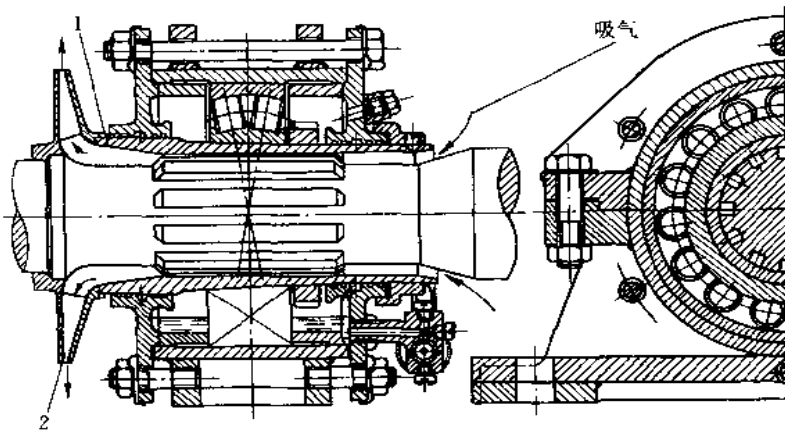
装在焊接座上的调心滚子轴承支承
